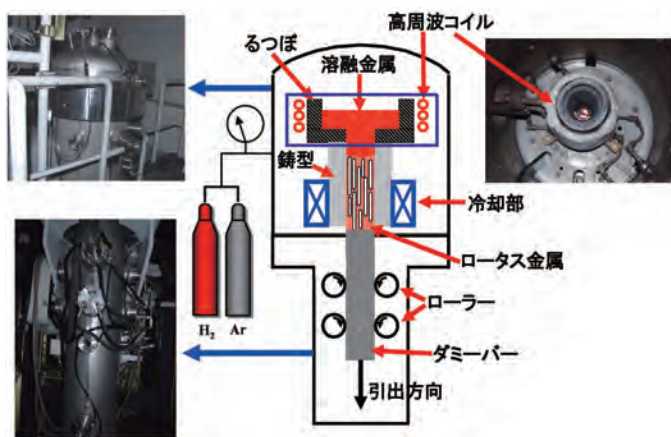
水素ガスを用いた連続 casting 装置の模式図と写真
